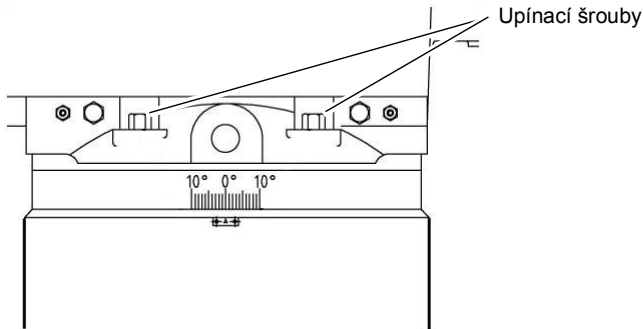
Pohyb unašeče frézovací hlavy vpřed / vzad
